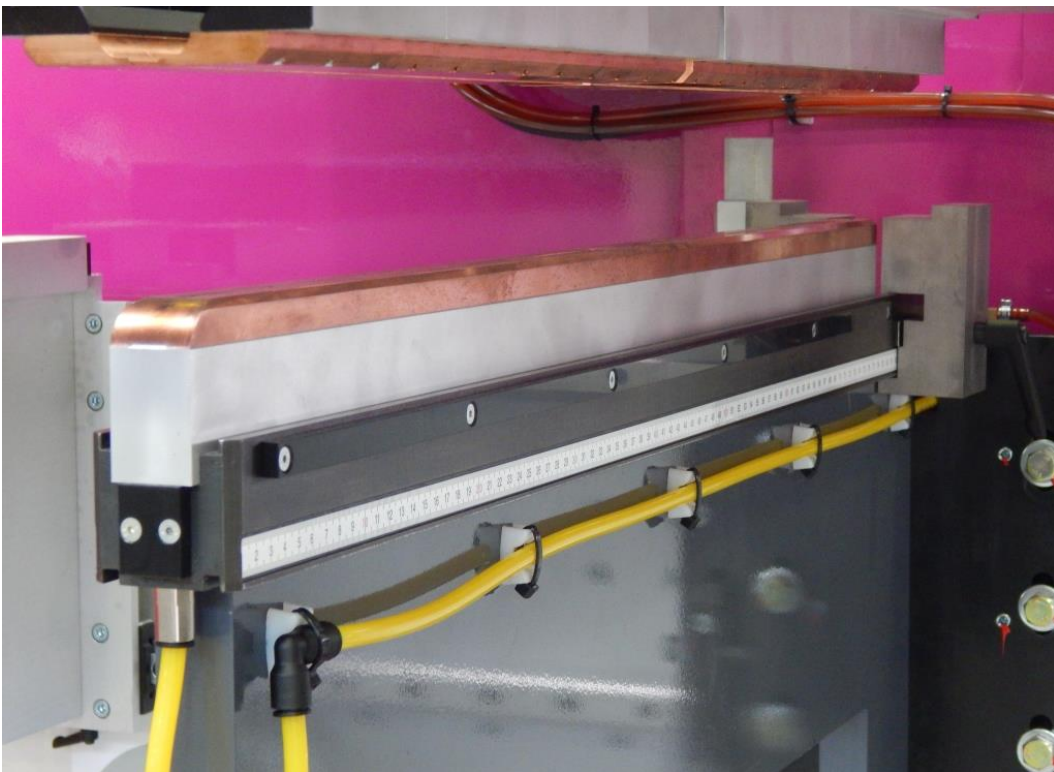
Schmäler Auflageholm mit CuCrZr Schweißunterlagschiene, Kühlung und Teilstop.
